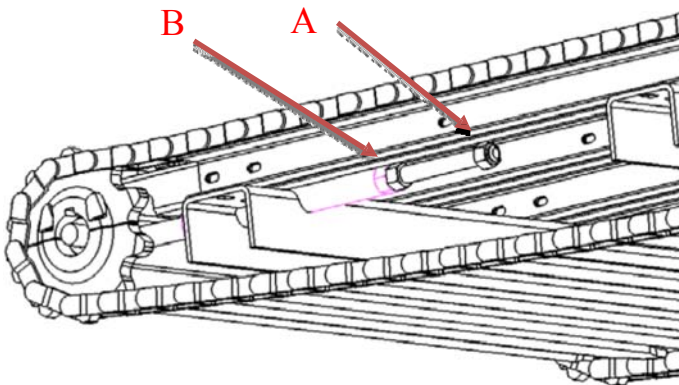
Вид цепи транспортера с регулировочными стержнями в разрезе
